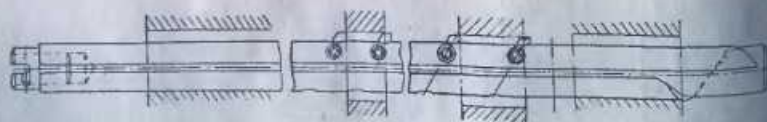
Борштанга ЛМ9417-082 для расточки постелей верхней части картера под коренные вкладыши
